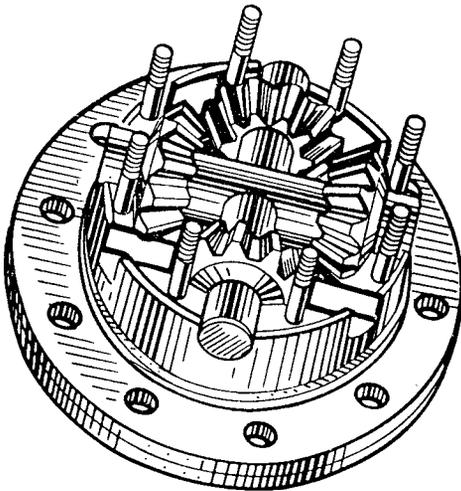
Einbau des Planetenträgers in das linke Ausgleichgehäuse
